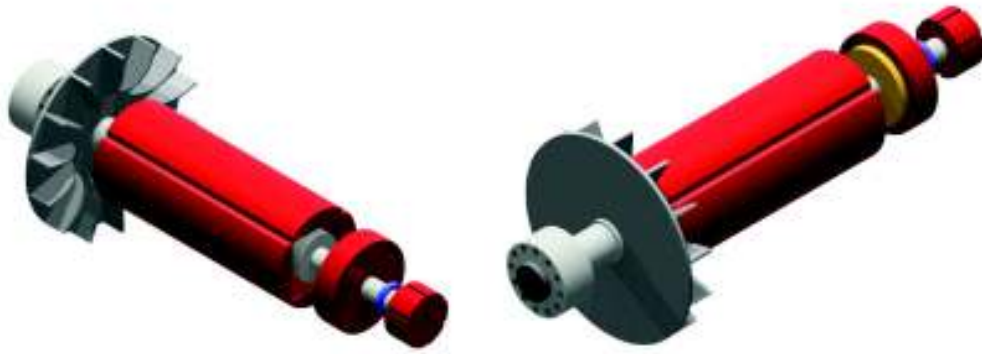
Conjunto rotórico de la máquina sincrónica. a) Vista superior, descripción de las artes.
